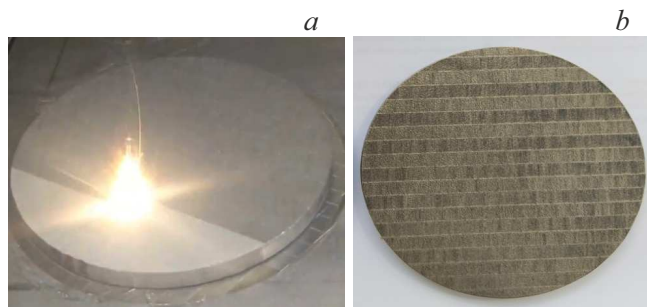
а) Лазерная обработка напыляемой поверхности и б) тип обрабатываемой поверхности.
